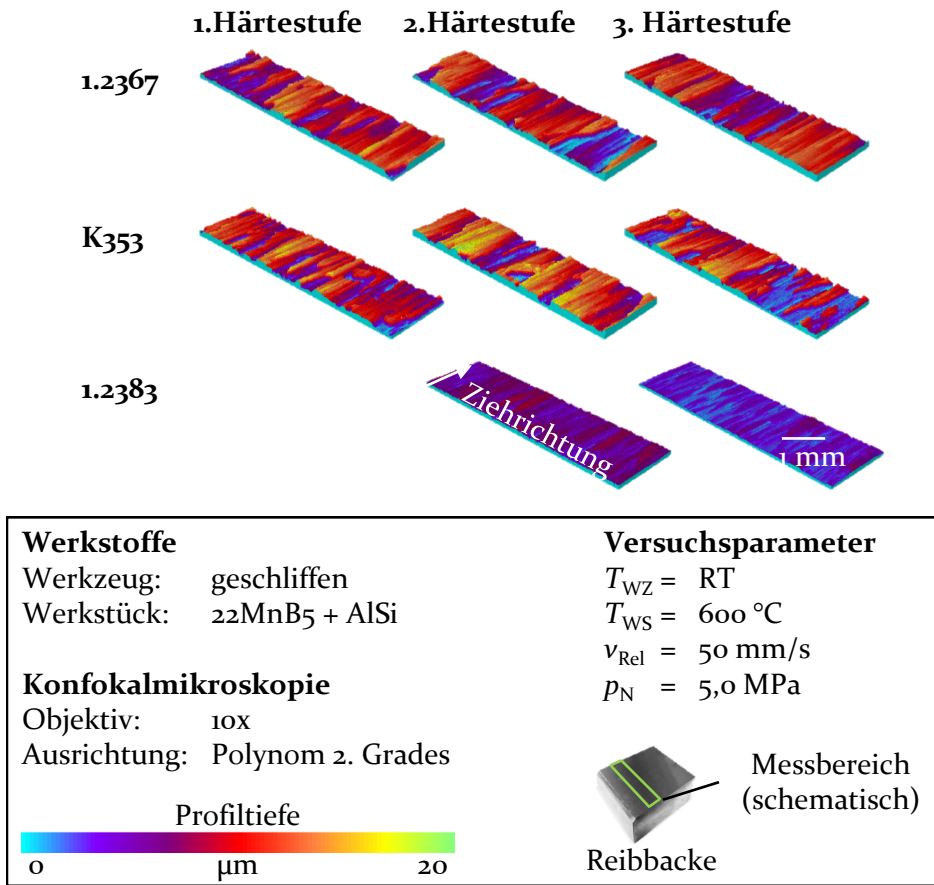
Topographieaufnahmen der Werkzeugoberfläche für unterschiedliche Werkzeughärten
